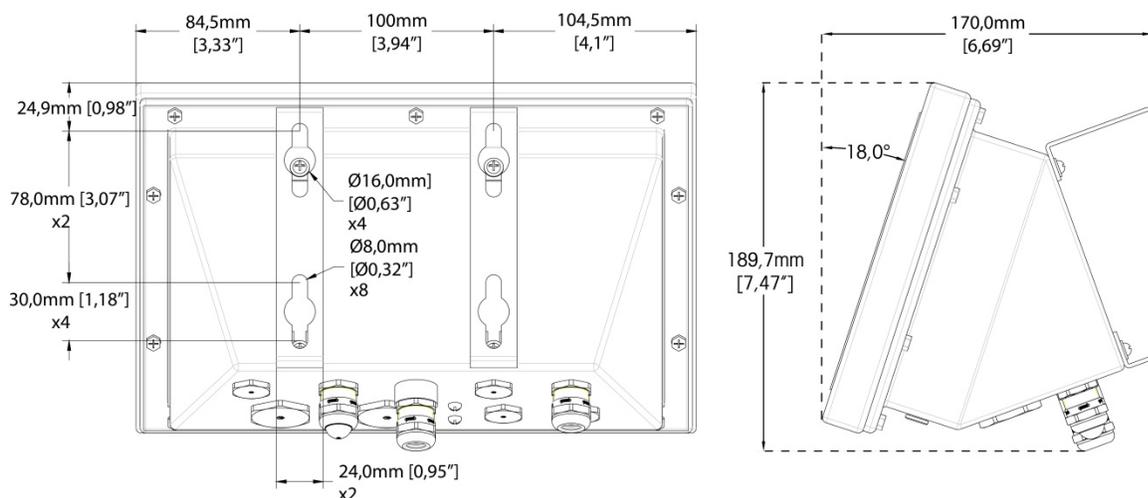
Dimensões do gabinete para ambiente adverso IND570xx com suportes de montagem de ângulo fixo, originais padrão de montagem
